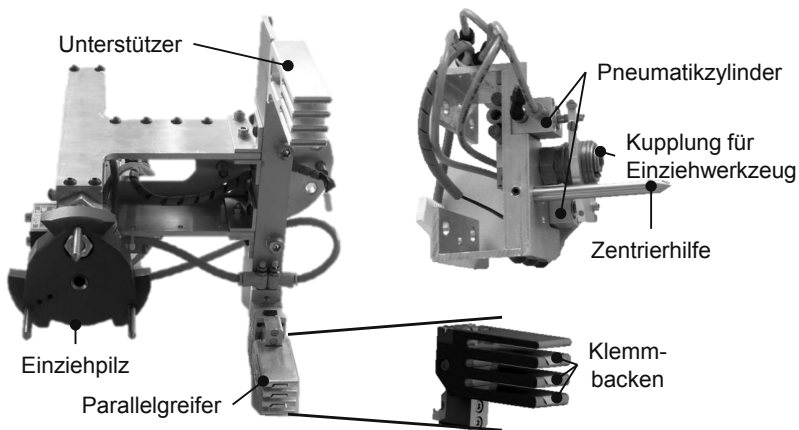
Einziehgreifer (links) und Zugwerkzeug (rechts oben)
